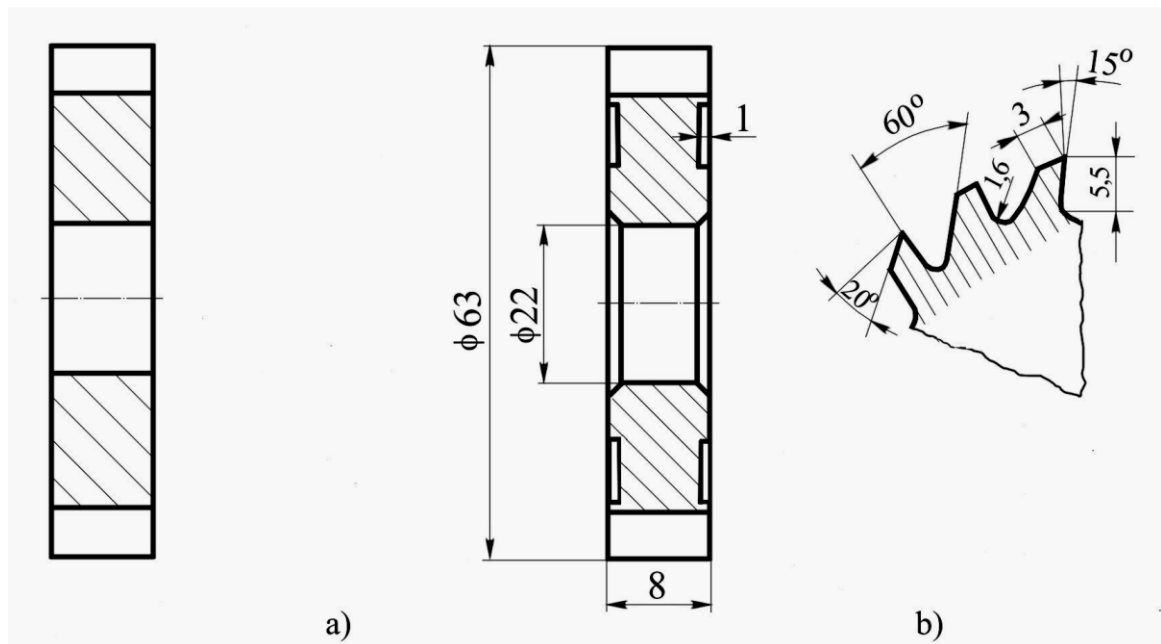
Dimensiunile și geometria frezei disc testate
